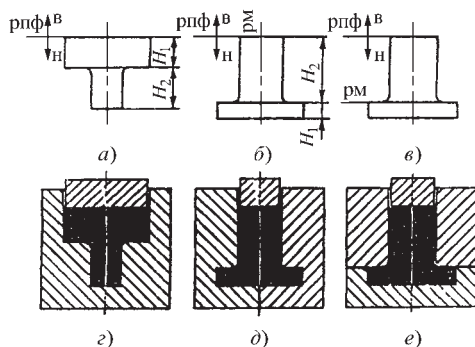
Заготовки (а–в) и схемы прессования (г–е): рпф — разъем пресс-формы; рм — разъем матрицы
